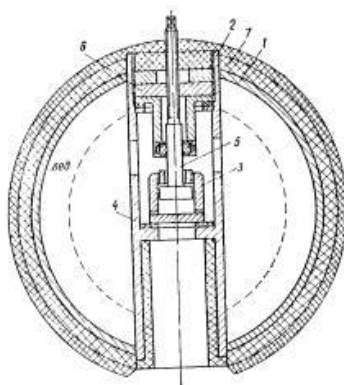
Конструкция аэрационного клапана при оледенении трубопровода на 50 % (1 - трубопровод; 2 - корпус арматуры; 3 - клапан; 4 - уплотнение; 5 - шпindelь; 6 - нажимная гайка; 7 – теплоизоляция)
